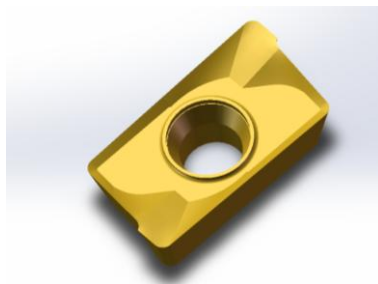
3D модель режущей пластины фрезы
